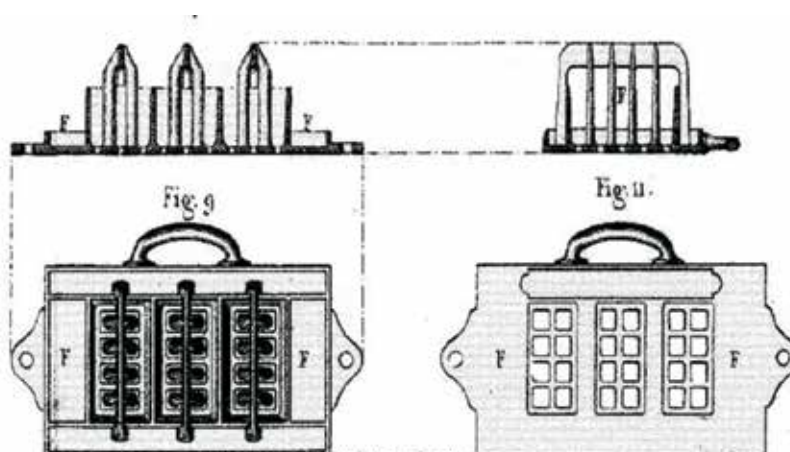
Vistas de uma boquilha da máquina de M. Borie, 1857.
